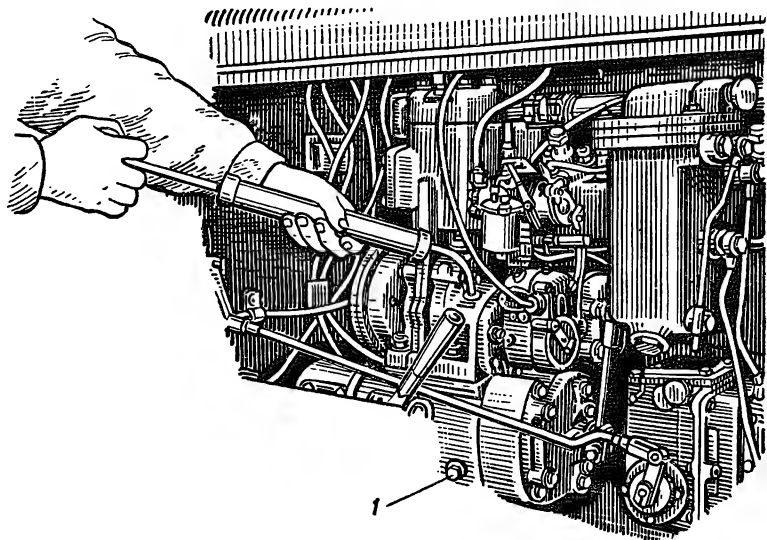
Заправка масла в картер приводного механизма пускового двигателя:
